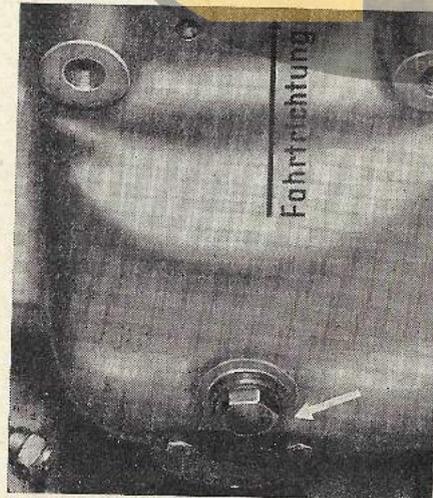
Ölablaßschraube an der Getriebeunterseite
